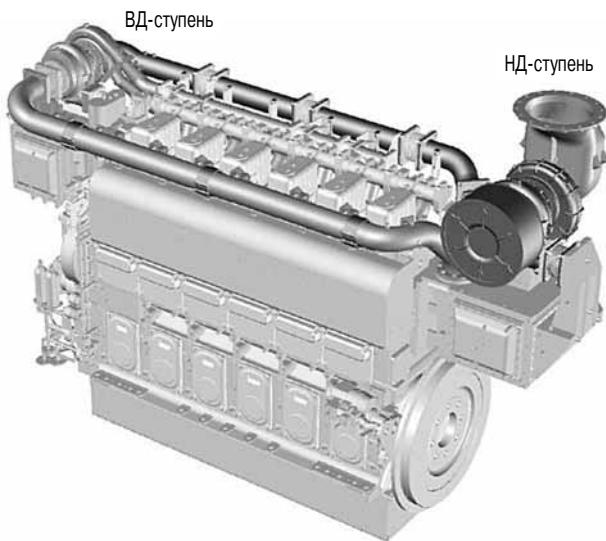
Главный пропульсивный двигатель с ДСН К2В
